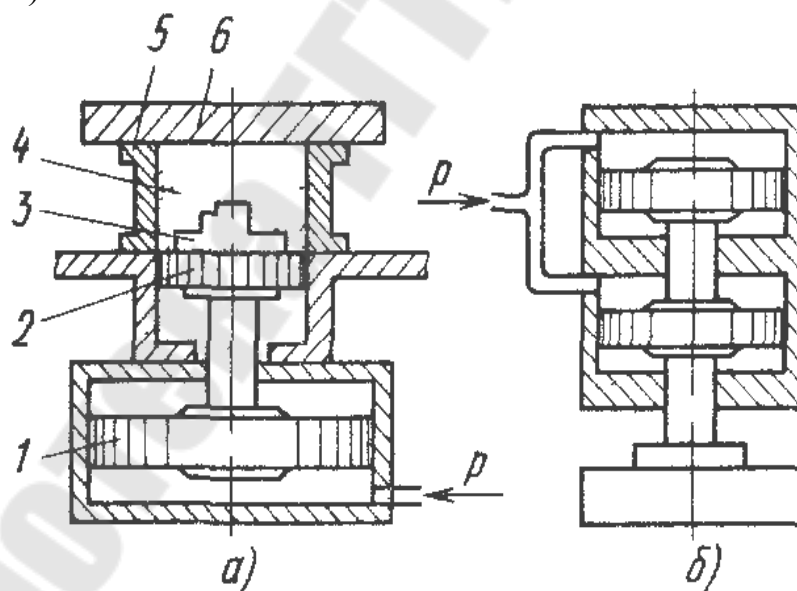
Схемы поршневых приводов: а - пневмоцилиндр большого диаметра; 1 - силовой поршень с цилиндром; 2 - подвижная модельная плита; 3 - модель; 4 - смесь; 5 - опока; 6 - опорная плита; б - сдвоенный пневмоцилиндр
